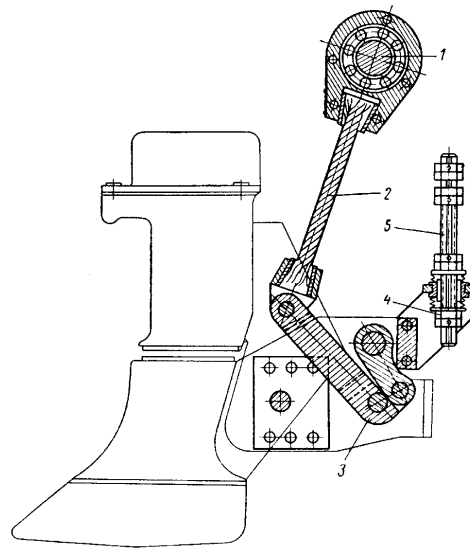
Корпус плуга з гнучкою ланкою для передачі коливань.
